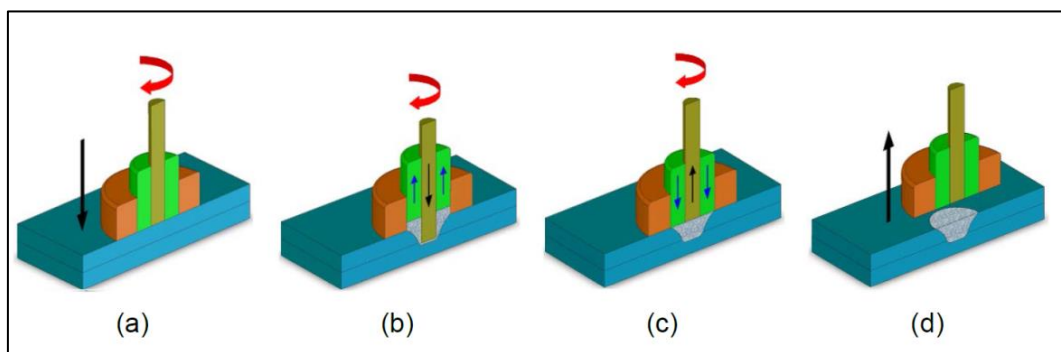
Esquema mostrando a variante *penetração do pino* do processo FSpW. a) aperto das chapas e rotação da ferramenta; b) penetração do pino e retração da camisa; c) ferramentas voltam à superfície; d) remoção da ferramenta. [9]
